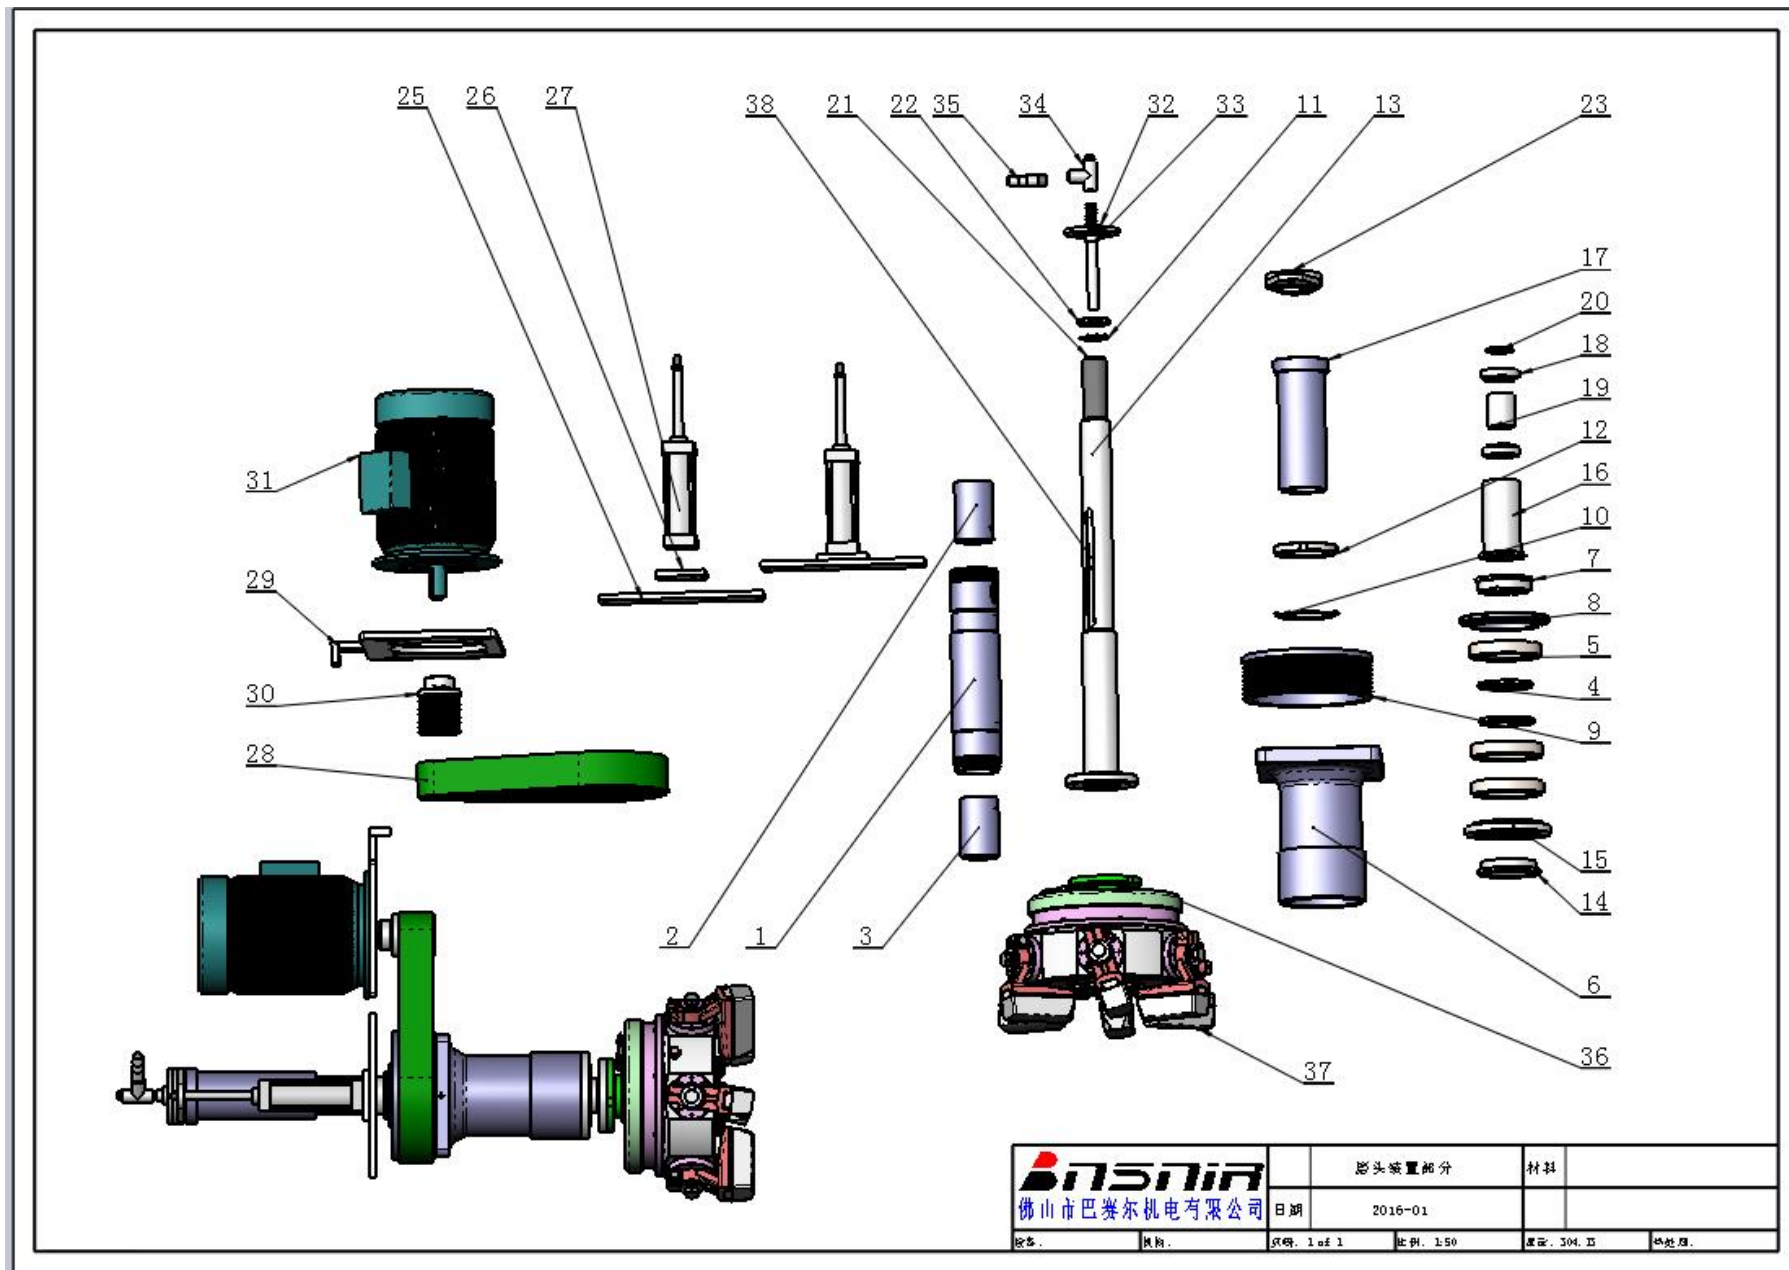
BP1000/16 抛光机——磨头上部及磨头部分装配图 picture6-1 BP1000/16 polishing machine -- Assembly drawing of grinding head and part of grinding head
